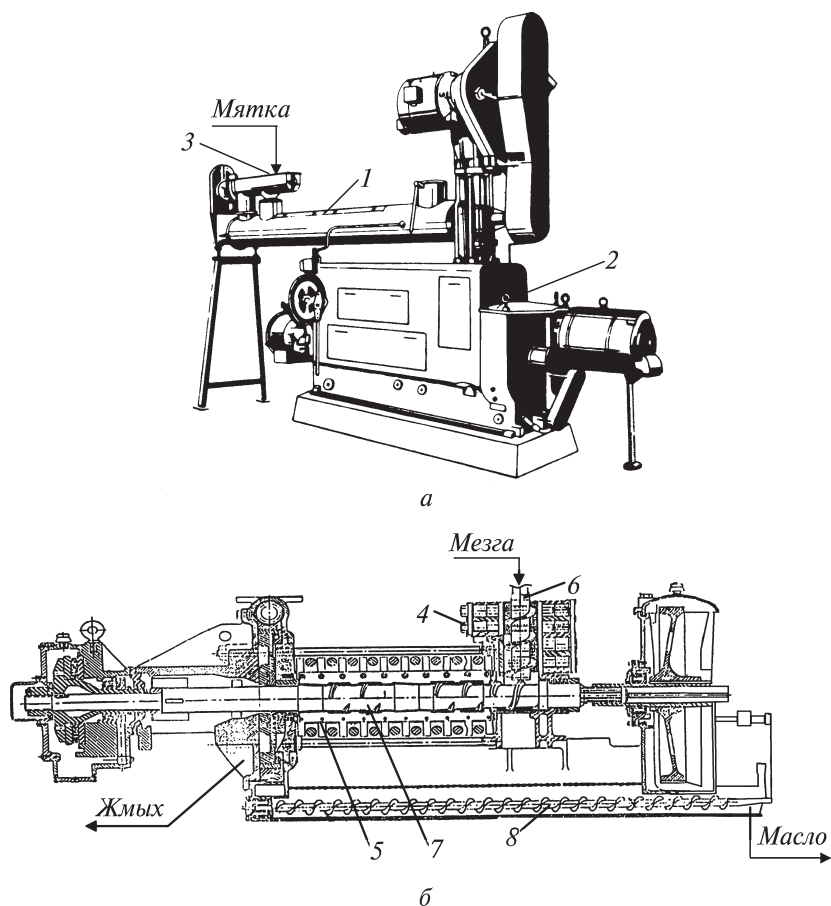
Прессовый агрегат фирмы «Андерсон»:
